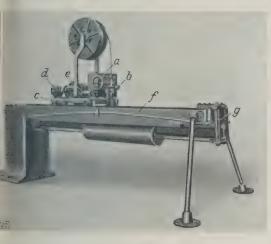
osttätige Längsnaht-Schweißmaschine der Westinghouse Electric & Mfg. Co.
